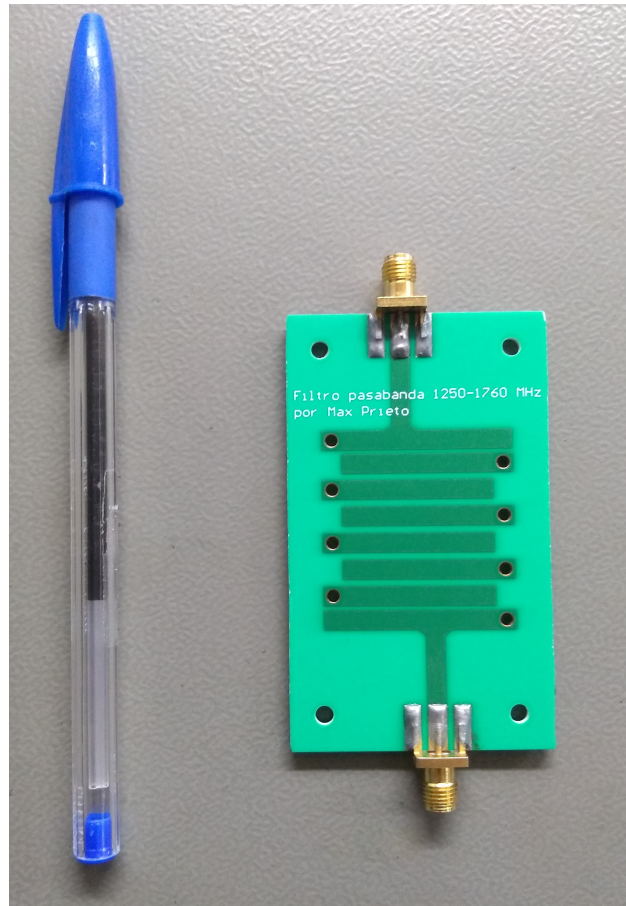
Filtro construido y con conectores SMA soldados.
